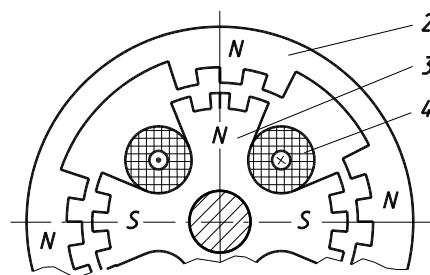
Конструкція МЕР з гребінцевими зонами з рухомих індуктором
